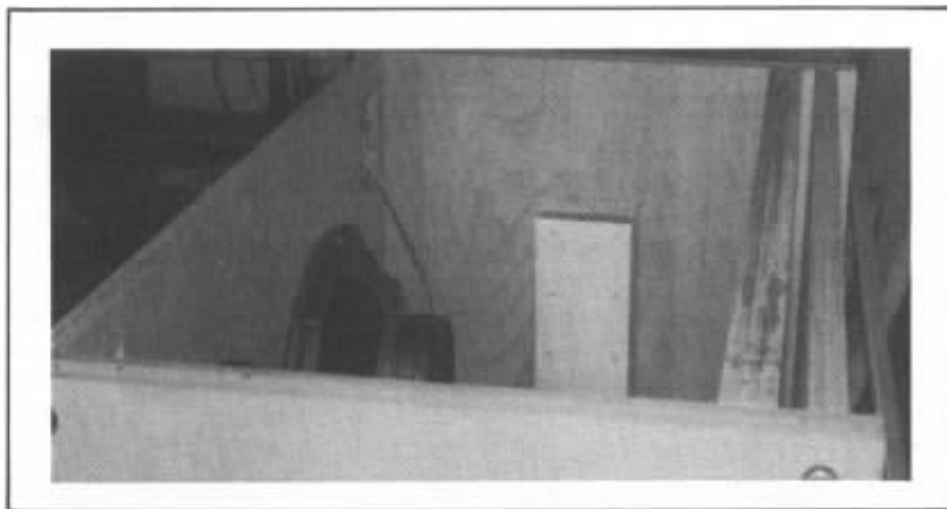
L'enceinte en cours d'assemblage révélant clairement la structure du fond. Il est nécessaire de positionner la face avant avant de fixer les deux parois du fond (sur cette photo le positionnement n'est pas définitif, il y a 30 mm d'espace entre les deux parois du fond pour le sablage). Naturellement, les haut-parleurs seront démontés pour la suite des opérations d'assemblage afin d'éviter tout accident.
